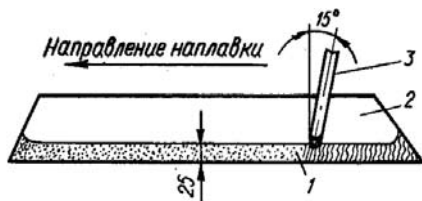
Схема электродуговой наплавки лезвия лемеха порошкообразным твердым сплавом: 1 — шихта; 2 — лемех; 3 — графитный электрод
